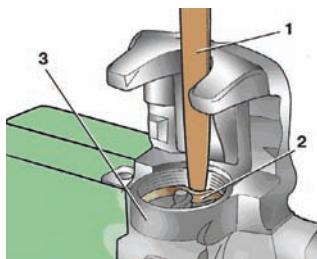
Удаление уплотнительного кольца из цилиндра суппорта.
